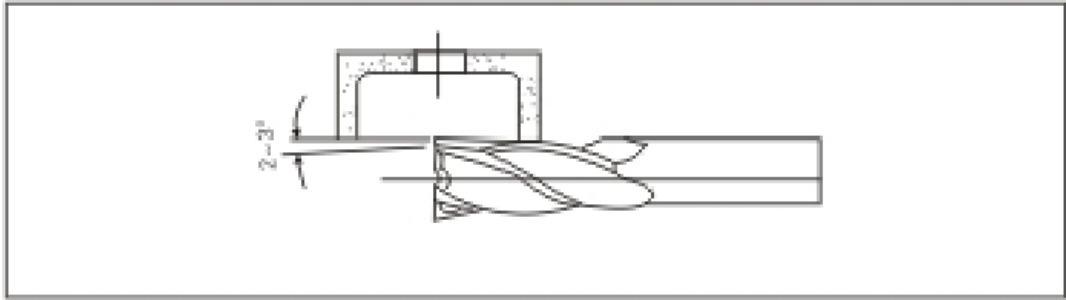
Схема сборки чашеобразного шлифовального круга
